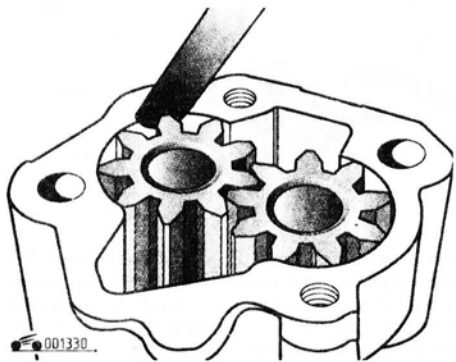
Проверка зазора между зубьями шестерен и корпусом масляного насоса
